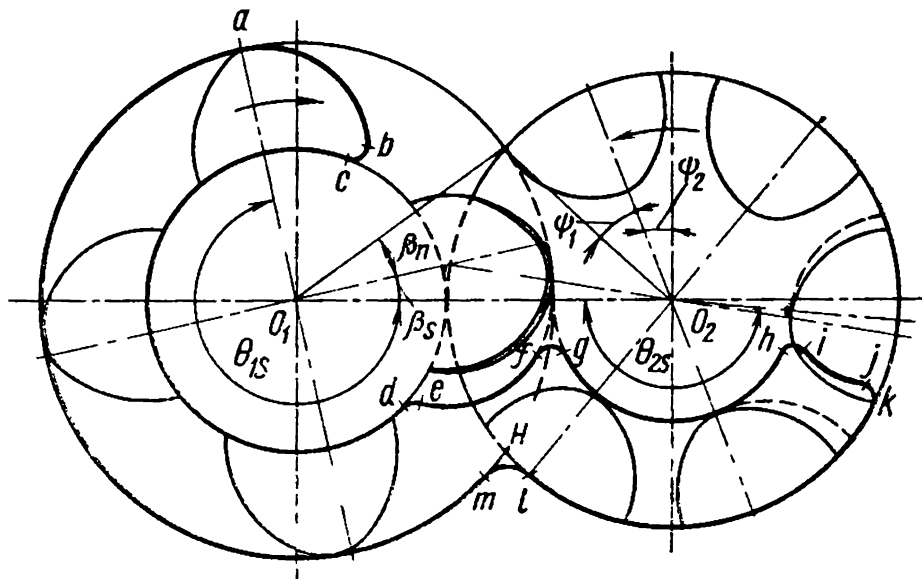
Схема расположения всасывающего окна винтового компрессора
